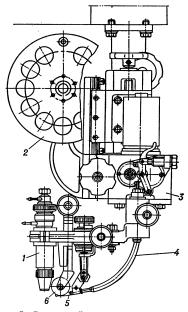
Сварочный полуавтомат для электросварки неплавящимся вольфрамовым электродом с подачей присадочной про-волоки: 1— горелка; 2— катушка; 3— механизм подачи; 4— направляющий шланг; 5— наконечник; 6— прижимной ролик.
